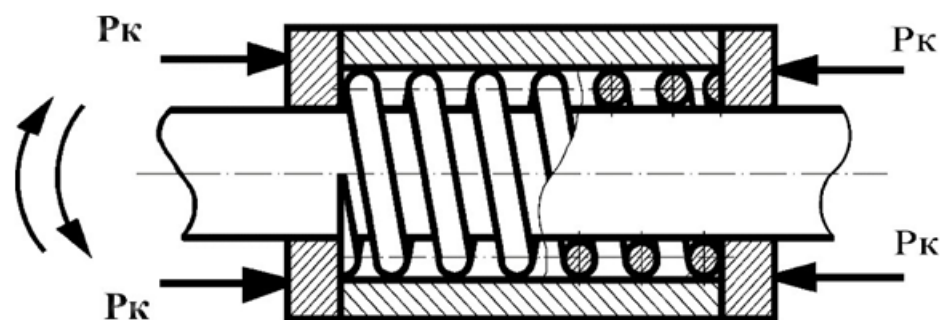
Схема підшипника з рухомих пружинним вкладишем
